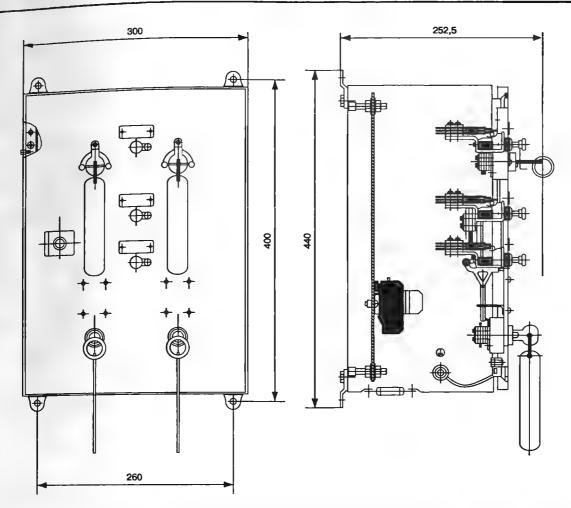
Габаритные и установочные размеры пульта ключей-жезлов ПКЖ-1, черт. 17481-00-00-01
